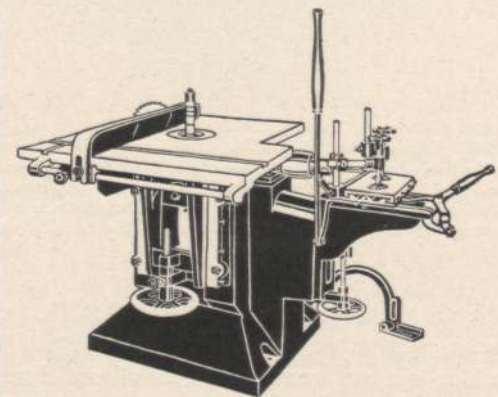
Kombinierte Kreissäge und Tischfräse mit Langlochbohrvorrichtung (auf Eisenbetonfuß montiert.)
